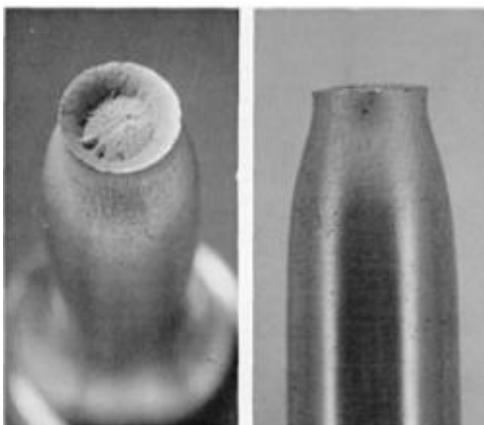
Vista macroscópica da fratura dúctil. Fonte: American Society [6].
